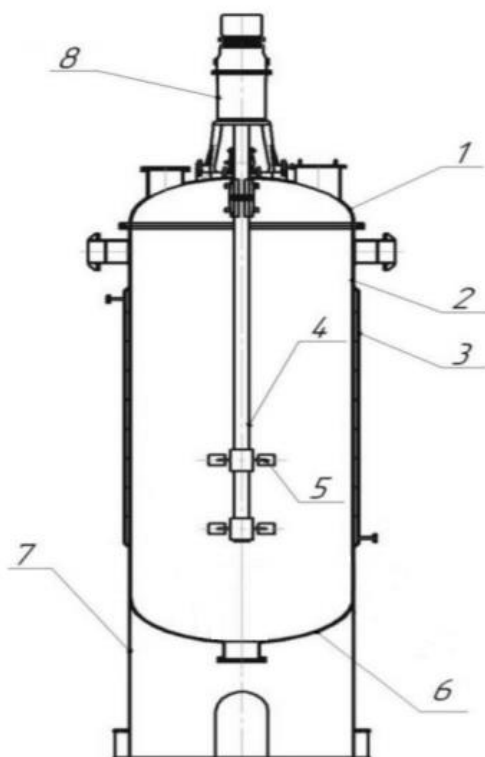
Схематичне зображення посівного апарату [82] 1 – кришка; 2 – корпус; 3 – сорочка; 4 – вал; 5 – перемішуючий пристрій; 6 – днище; 7 – опора, 8 – привід
